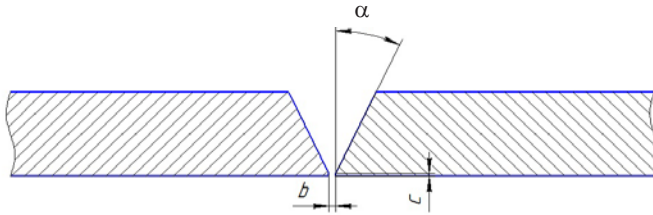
Параметры подготовки и сборки свариваемых пластин:
